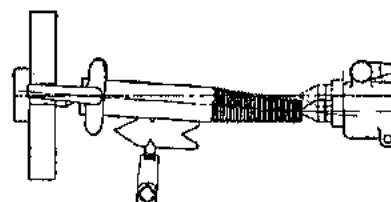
Cuando se tallan rosas cónicas, la cuchilla debe colocarse perpendicular al eje de la pieza (South Bend Lathe Works).
